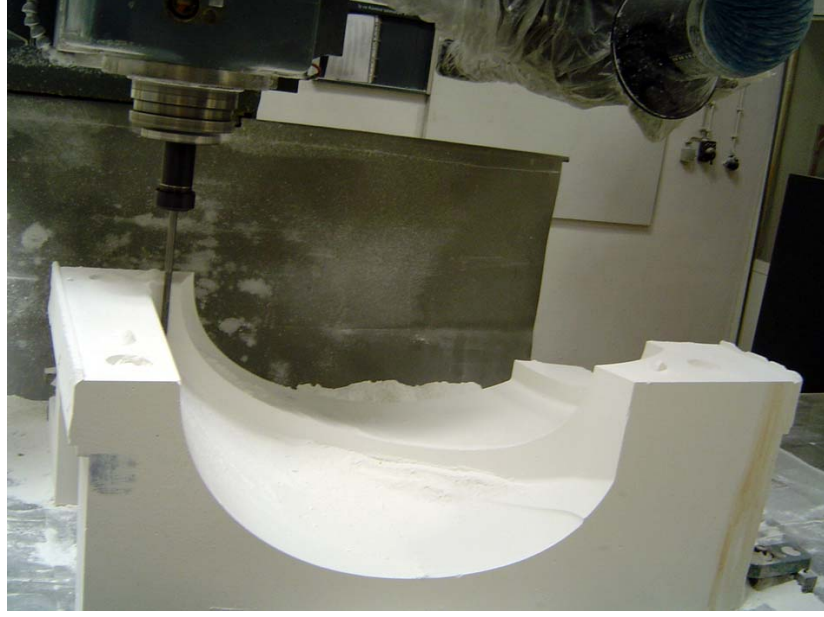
Mal alma kasnağı ve çekirdeklerin rötüşlanmamış görünümü
